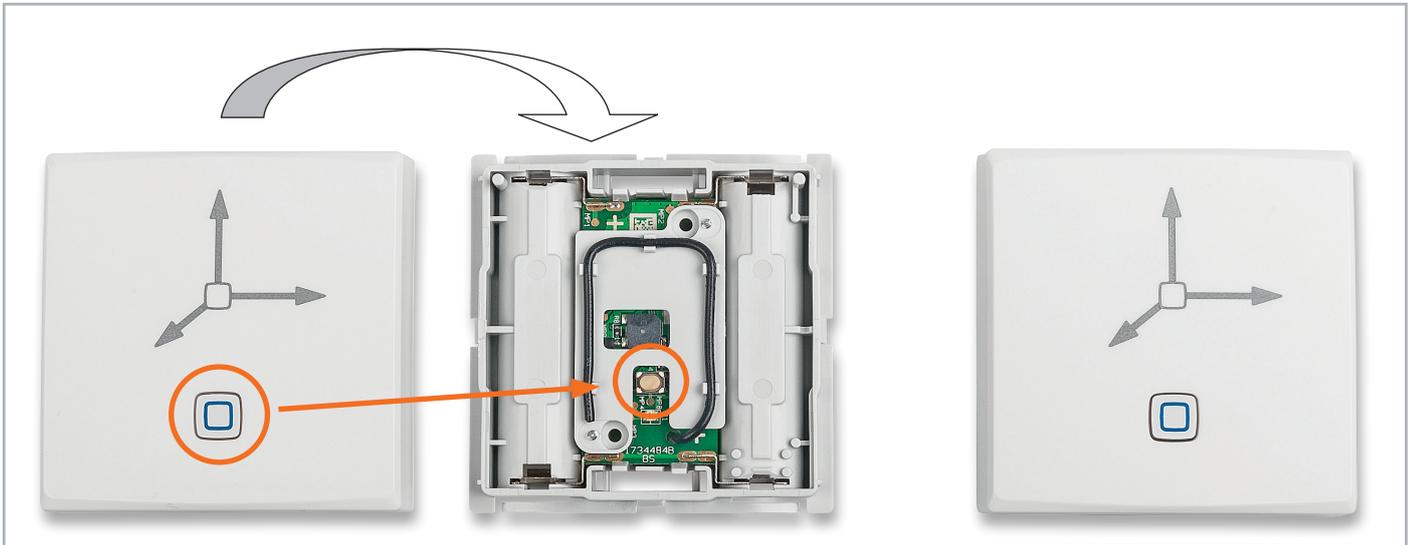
Mit dem Aufsetzen der Gehäuseoberseite ist die Montage abgeschlossen.
